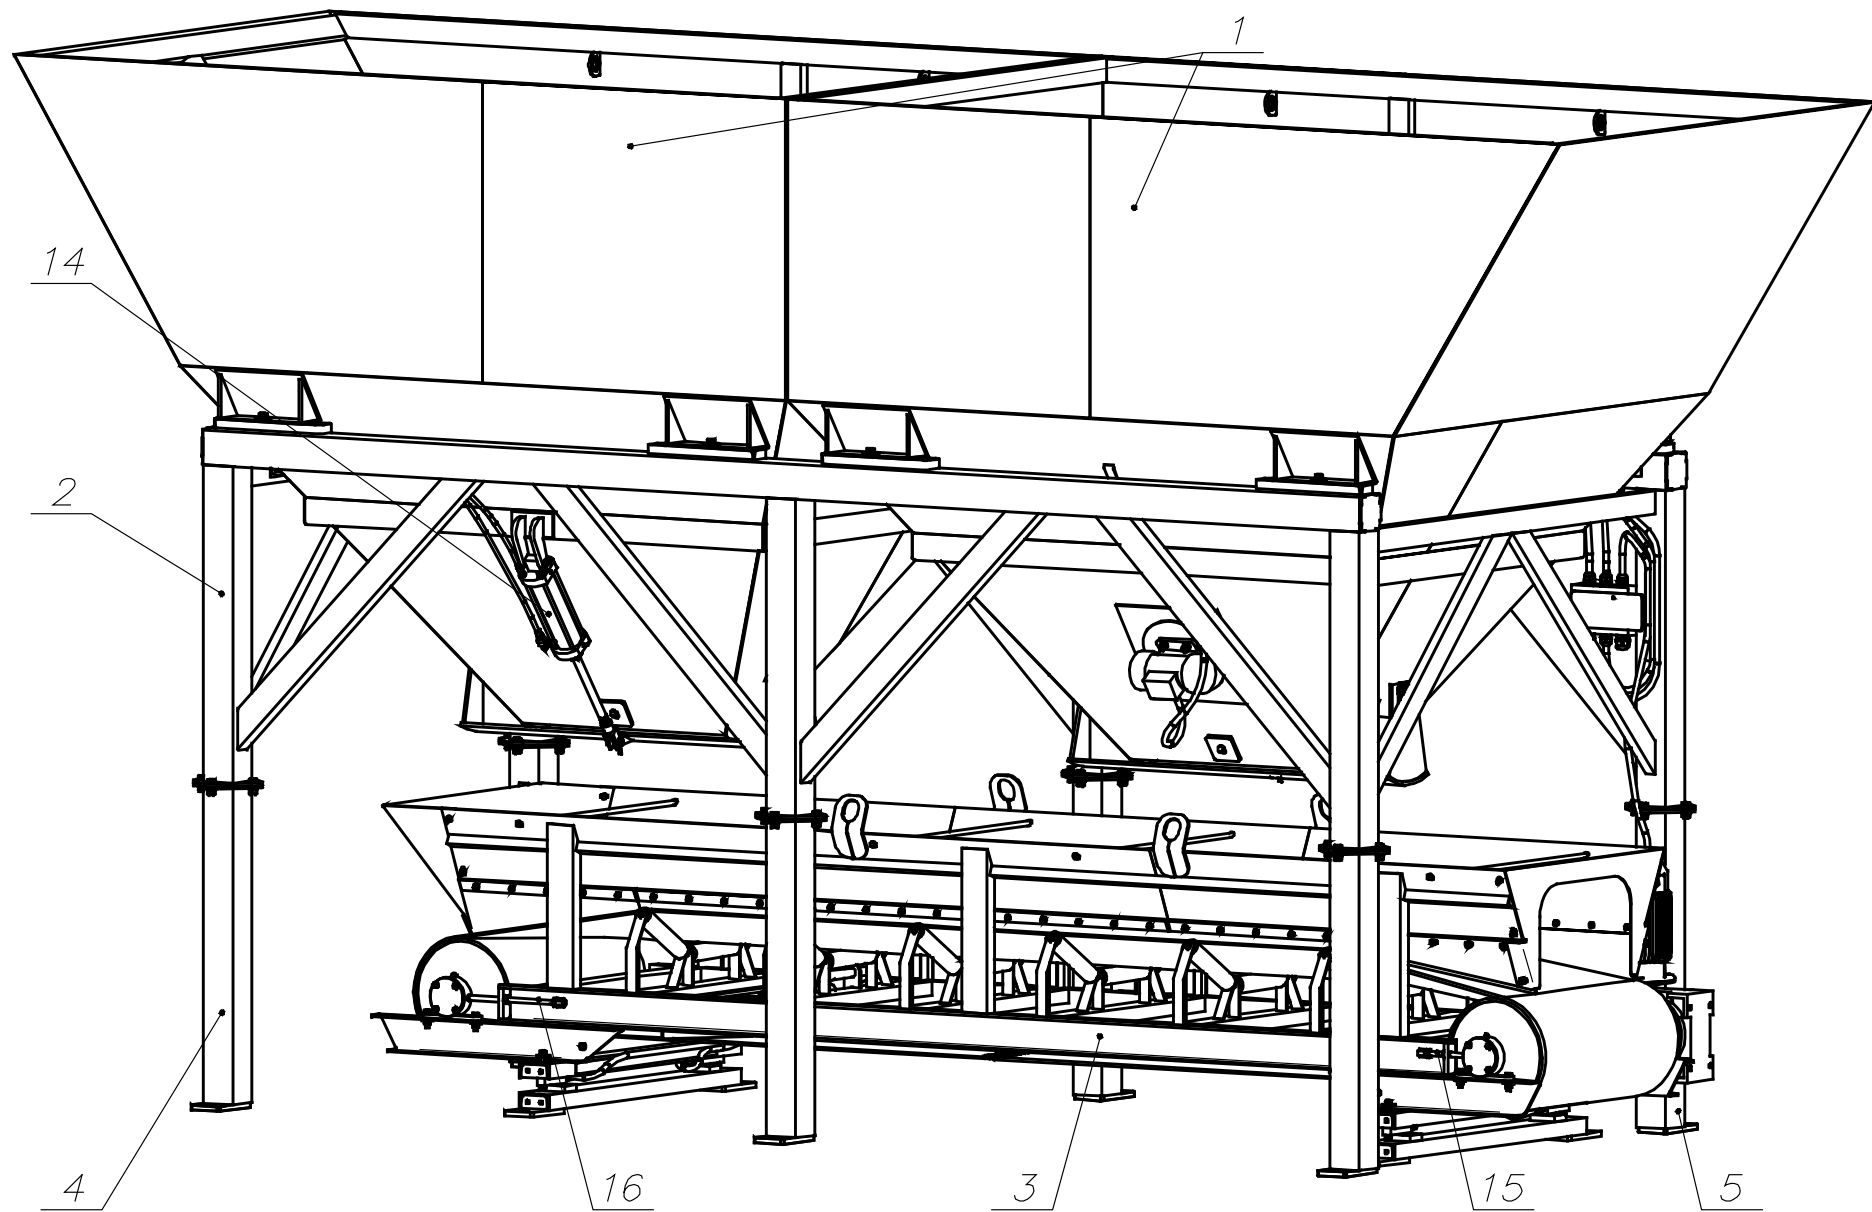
Общий вид дозатора ДЗ-15 вид спереди.
